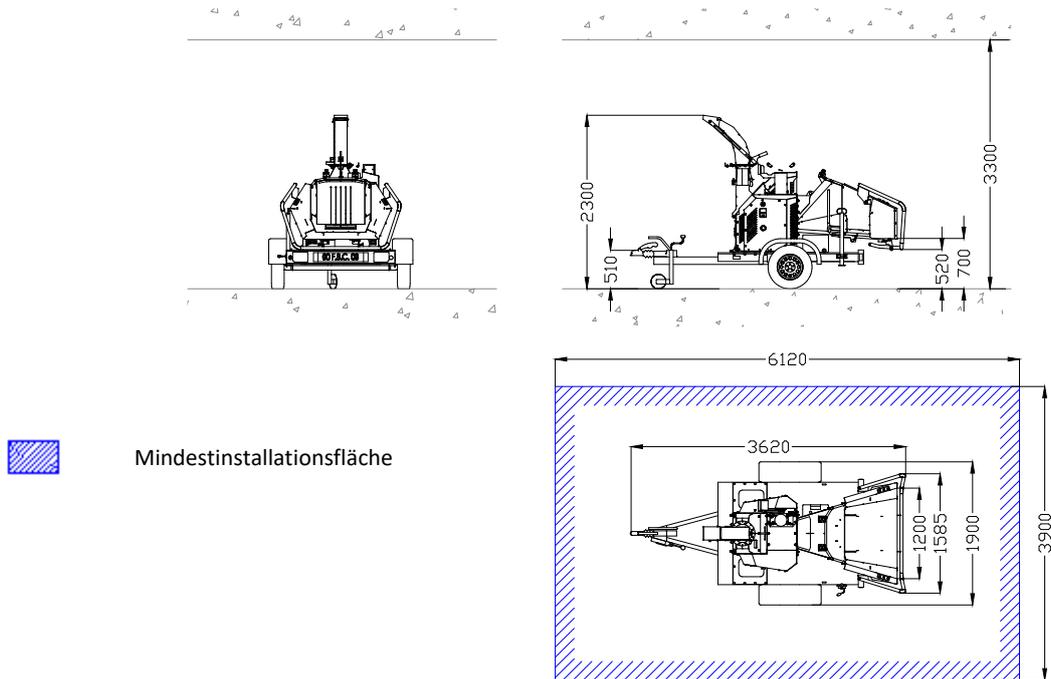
Mindestinstallationsfläche und Maschinenabmessungen
